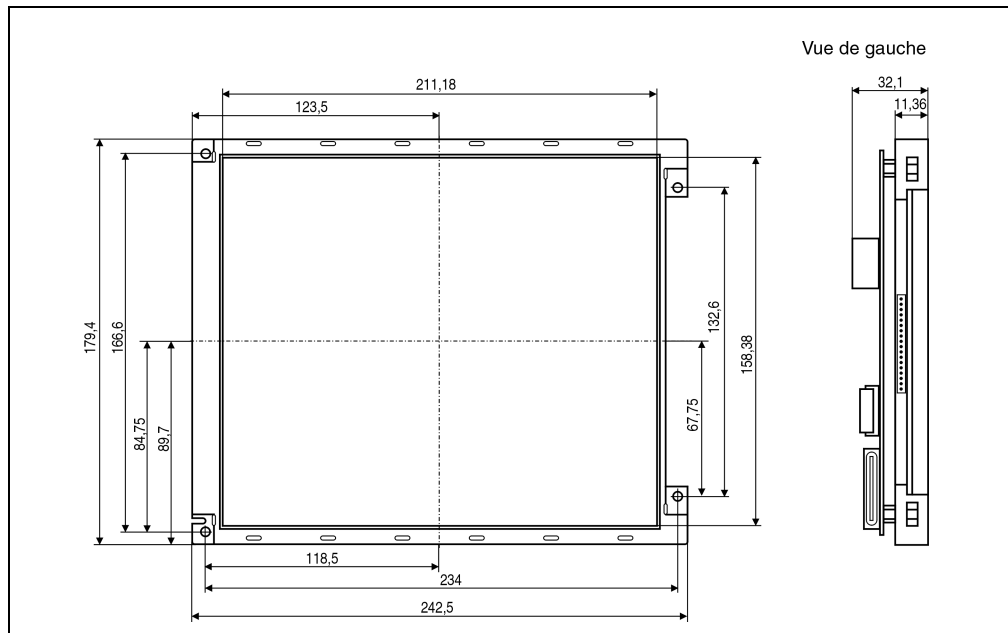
Dimensions 5D2000.10 (10,4 pouces)
